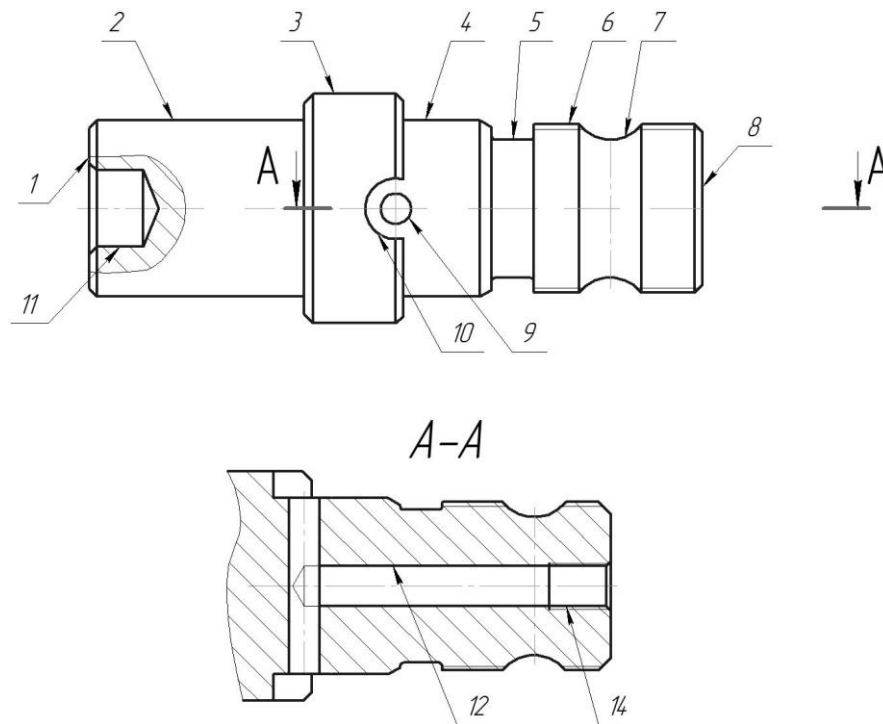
Ескіз деталі вал УЯИШ 716614.019
